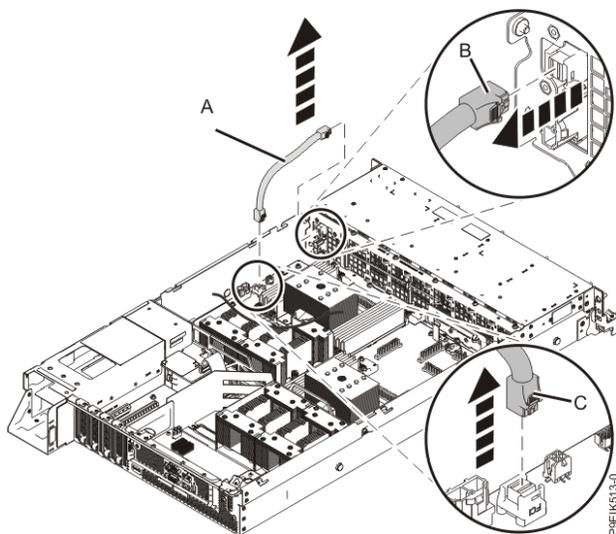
Removendo o cabo de sinal do disco e do ventilador
